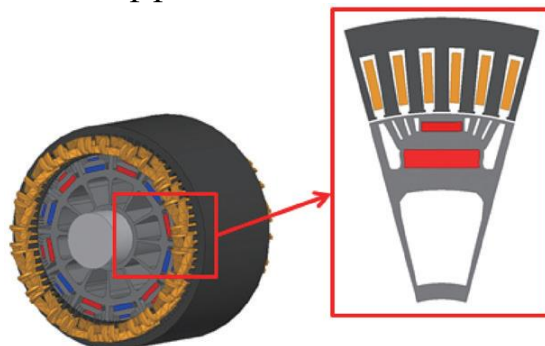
Приводной двигатель BMW i3 и форма ротора (IPMSM)
